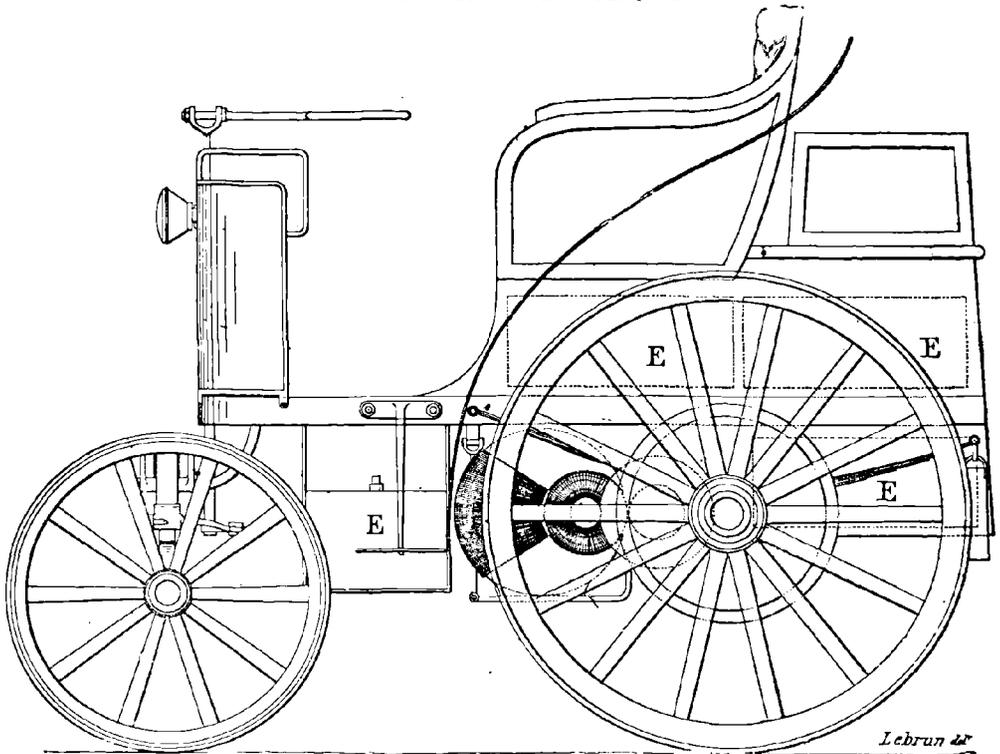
Première voiture Jeantaud (1881). — Elevation.
